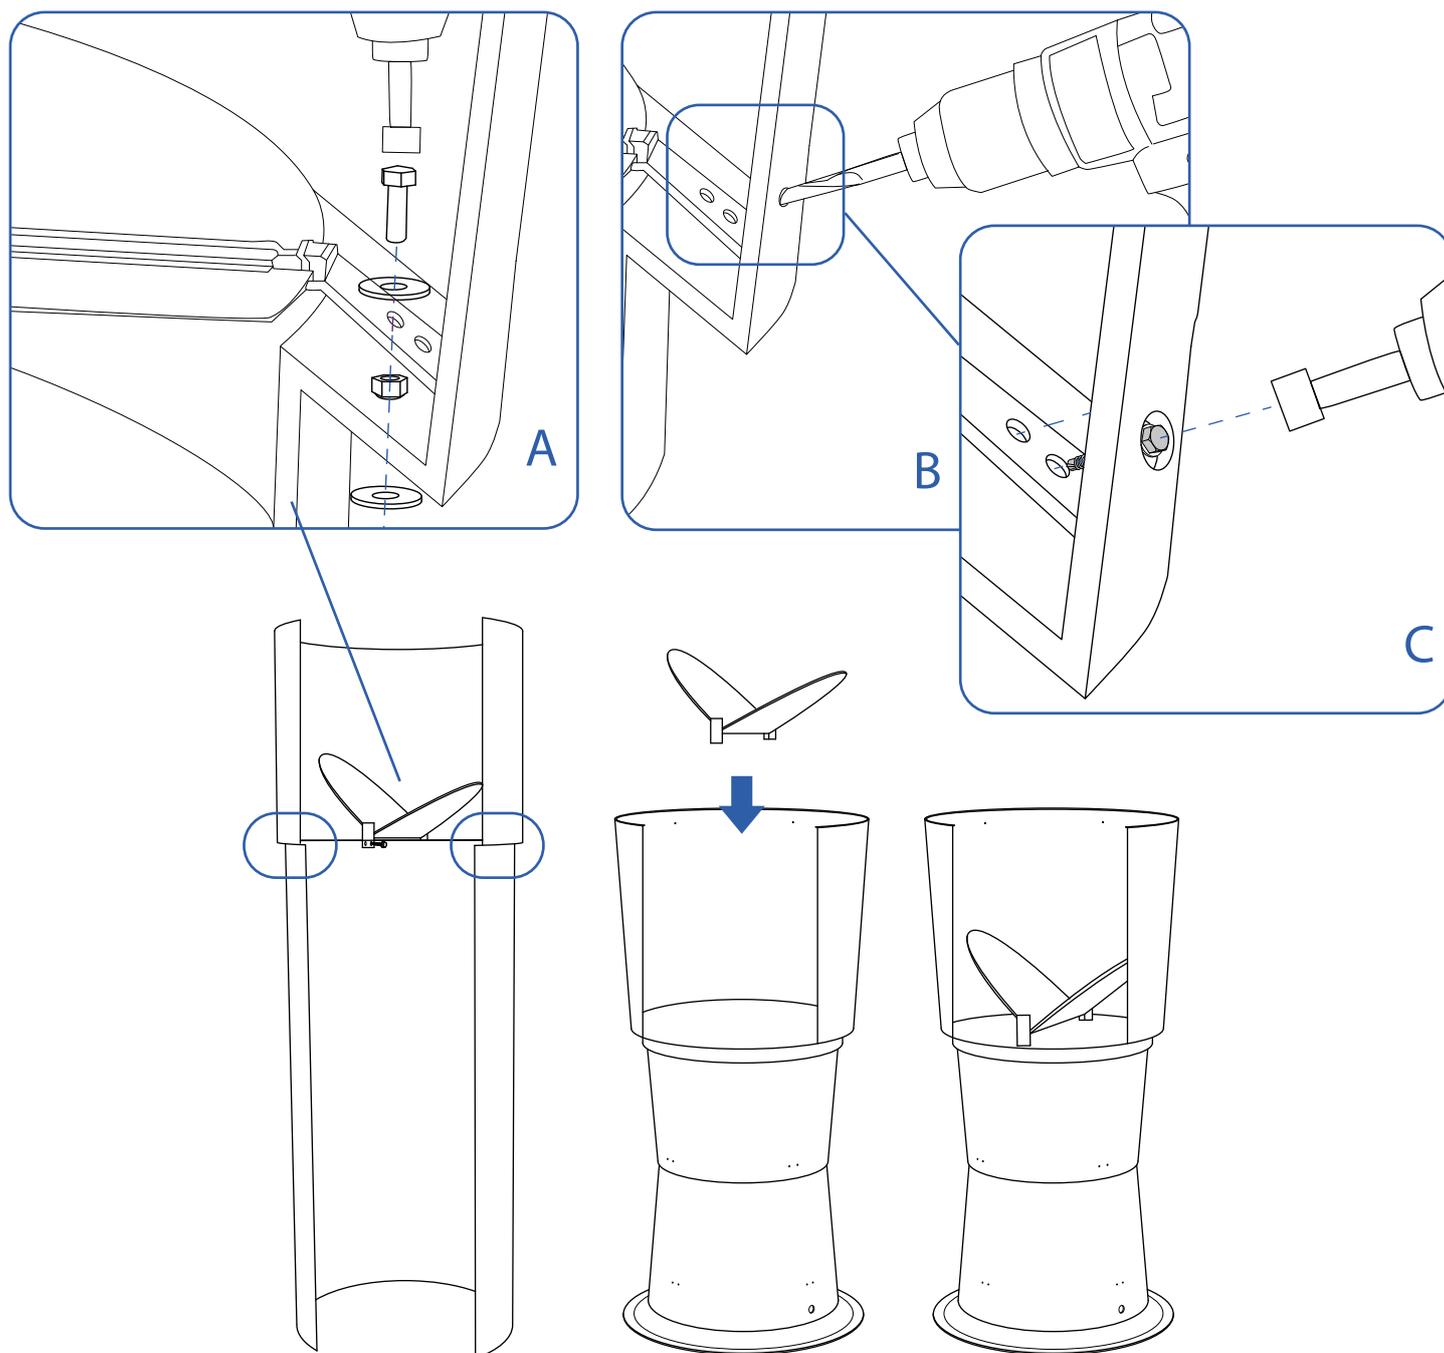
Montaje de la válvula de mariposa en las chimeneas rectas estándar y en las chimeneas cónicas apilables
